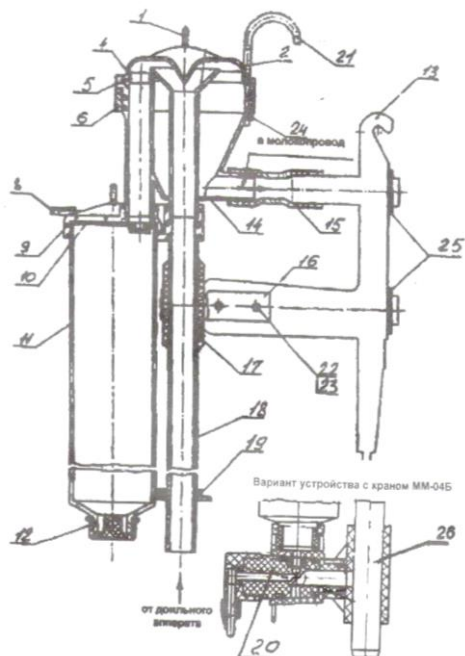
Общий вид устройства зоотехнического контроля молока ММ-04Б-01: 1 – скоба; 2 – крышка; 4 – насадка; 5 – кольцо; 6 – держатель; 8 – клапан; 9 – прокладка; 10 – клапан; 11 – колба; 12 – кнопка; 13 – ручка; 14 – корпус; 15 – патрубок; 16 – хомут; 17 – патрубок; 18 – труба; 19 – хомут; 20 – кран; 21 – кронштейн; 22 – болт; 23, 24 – гайка; 25 – прокладка; 26 – трубка.
